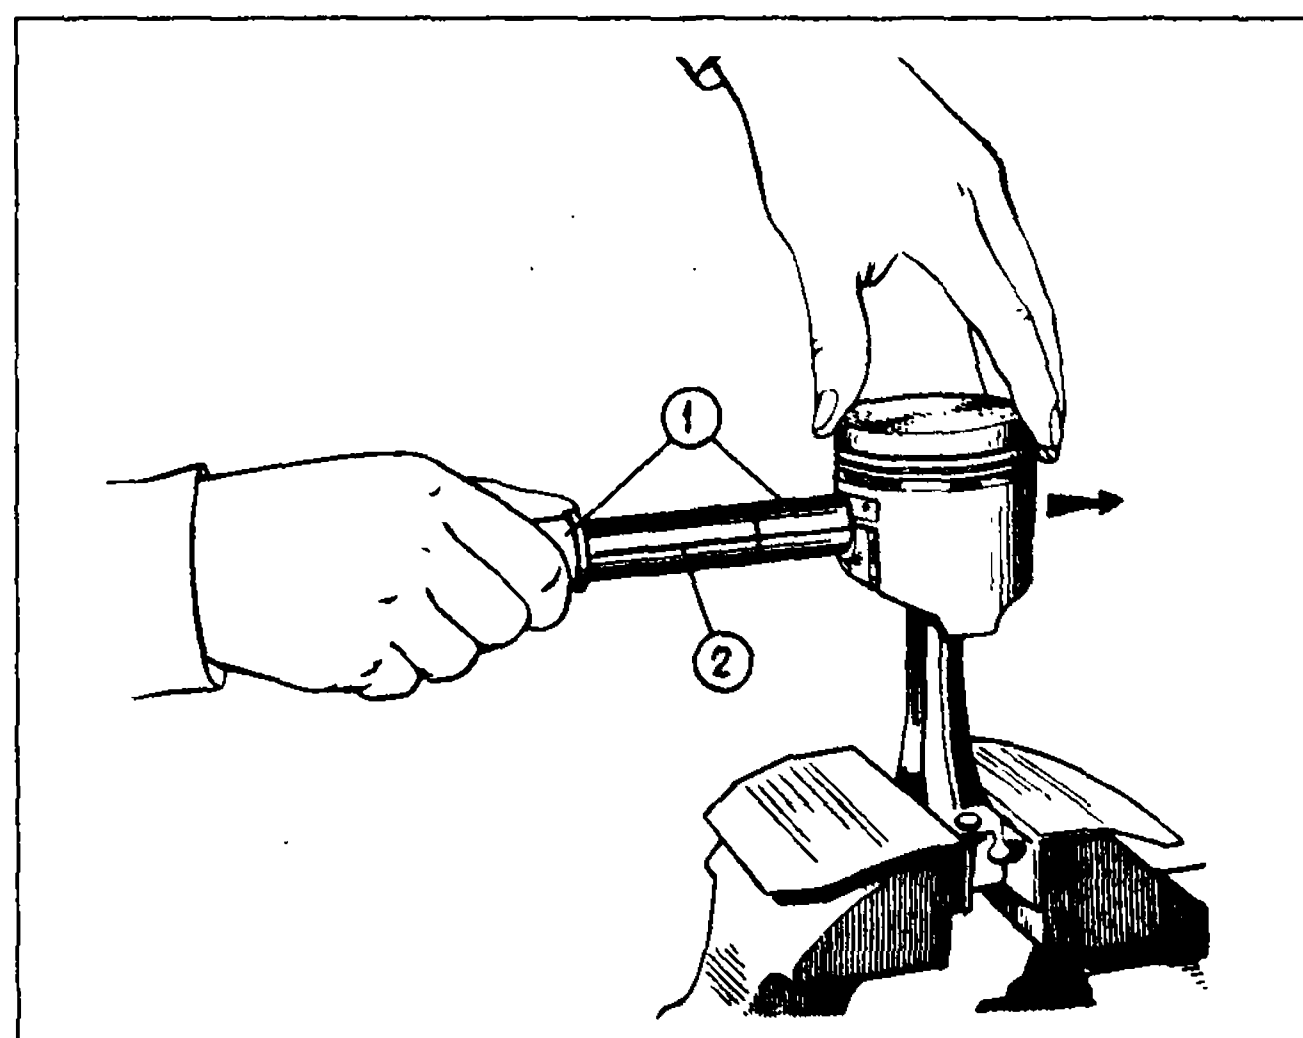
Запрессовка поршневого пальца в верхнюю головку шатуна: 1 - приспособление А.60325; 2 - поршневой палец. Поршень должен опираться на головку шатуна в направлении, указанном стрелкой
